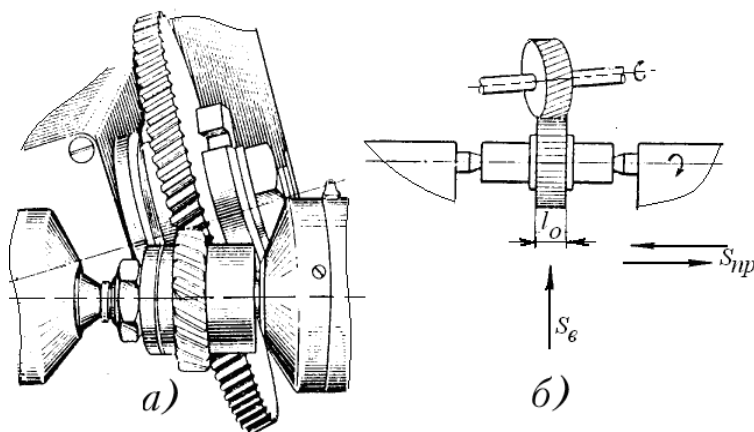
Шевінгування циліндричного зубчастого колеса дисковим шевером
